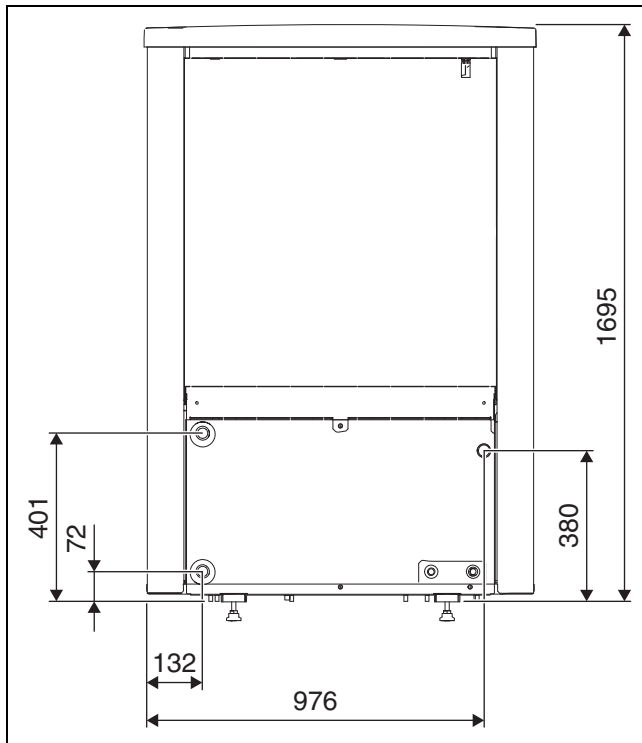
Dimensions et raccordements des modèles de pompe à chaleur 13-17, partie arrière
